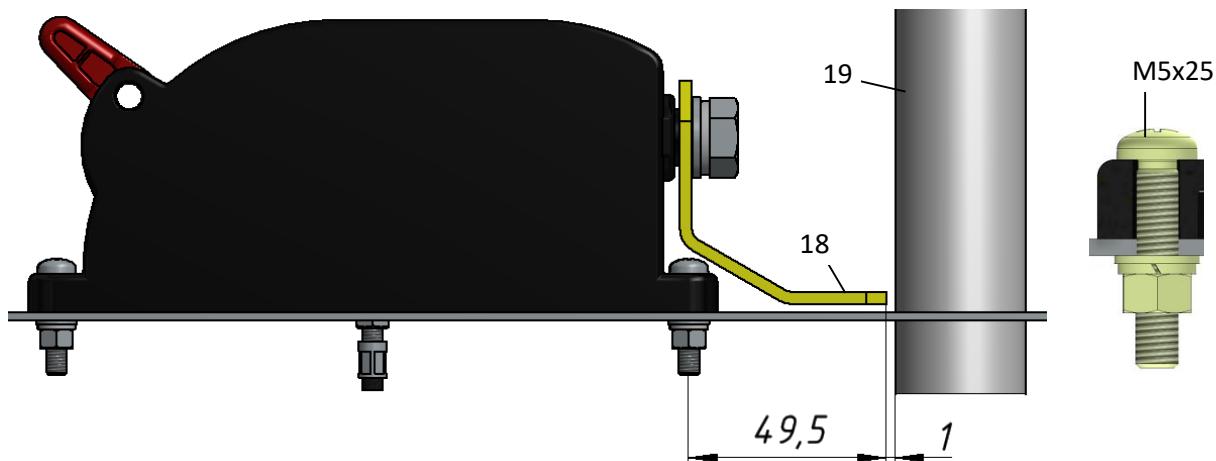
Установка блокиратора на ВЭ с червячным редуктором
